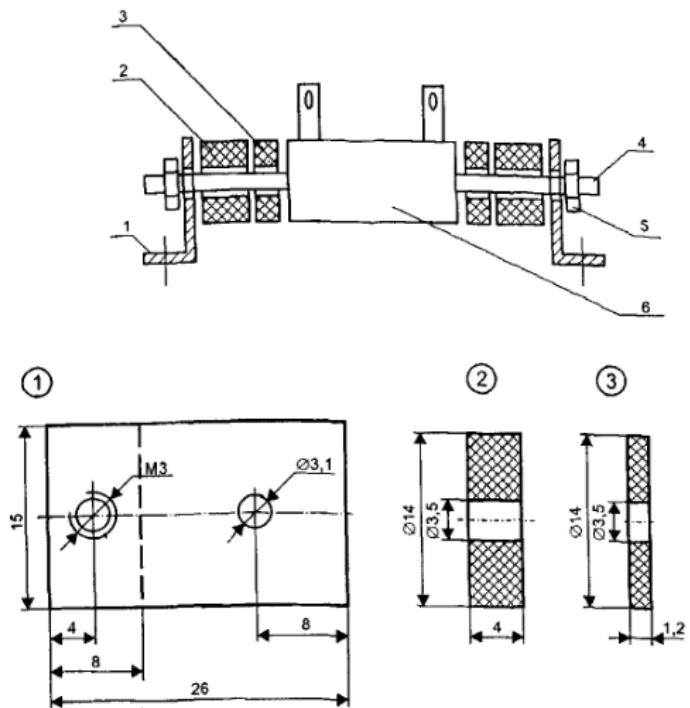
Крепление резистора R8 устройства задержки включения:
